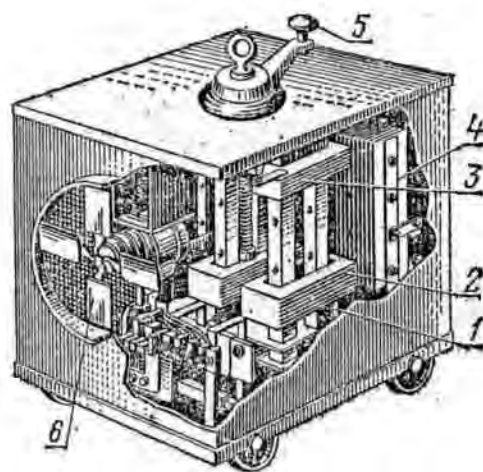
Сварочный выпрямитель ВСС-300-1:
